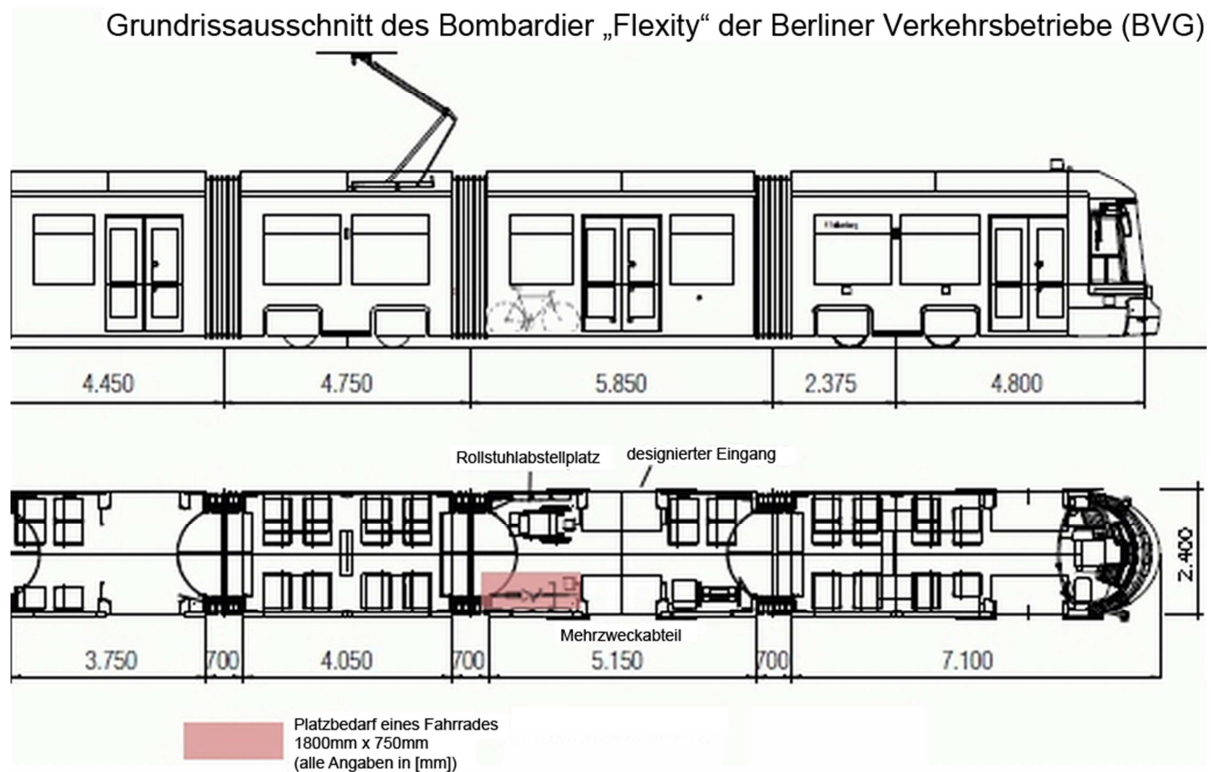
Grundrissausschnitt des Bombardier „Flexity“ der BVG (GT8-08 ZR)
